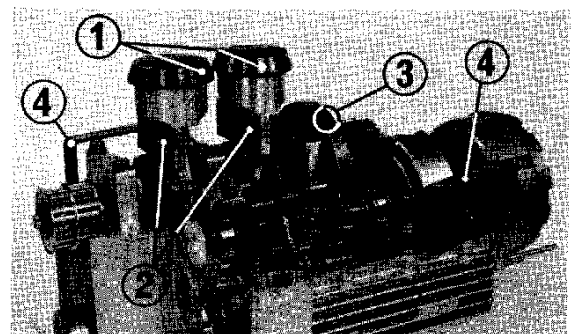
(1) Kolbenring-Einführwerkzeug
